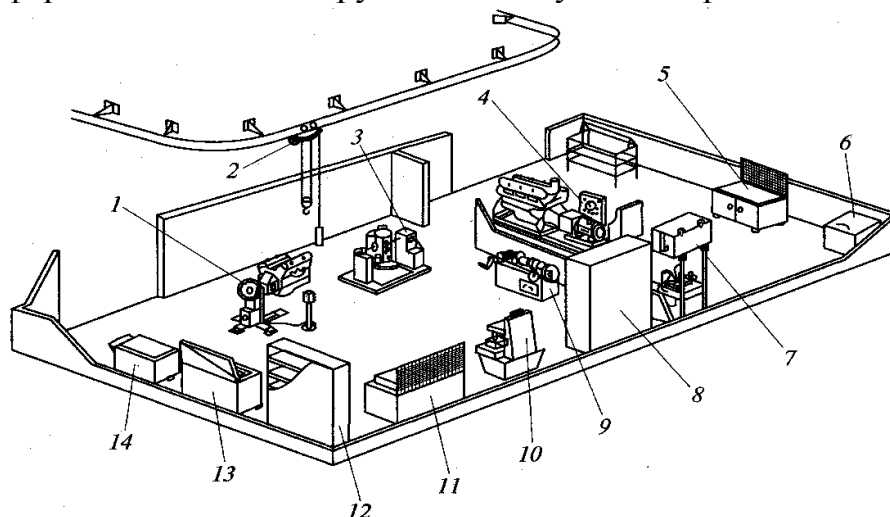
Участок ремонта и обкатки автотракторных двигателей: 1, 3 – стэнд для разборки и сборки двигателей; 2 – электроталь; 4 – стэнд обкаточно-тормозной КИ-5543М; 5 – верстак на одно рабочее место; 6 – ящик для песка; 7 – весовое устройство к стэнду; 8, 12 – стеллаж; 9 – стэнд для шлифовки клапанов Р-186; 10 – устройство для притирки клапанов Р-177; 11 – верстак с поворачной плитой; 13 – ванна моечная передвижная; 14 – гидрофицированная оснастка для текущего ремонта двигателей
